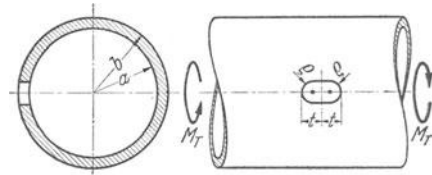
Hohlwelle mit Querbohrung (Langloch).
